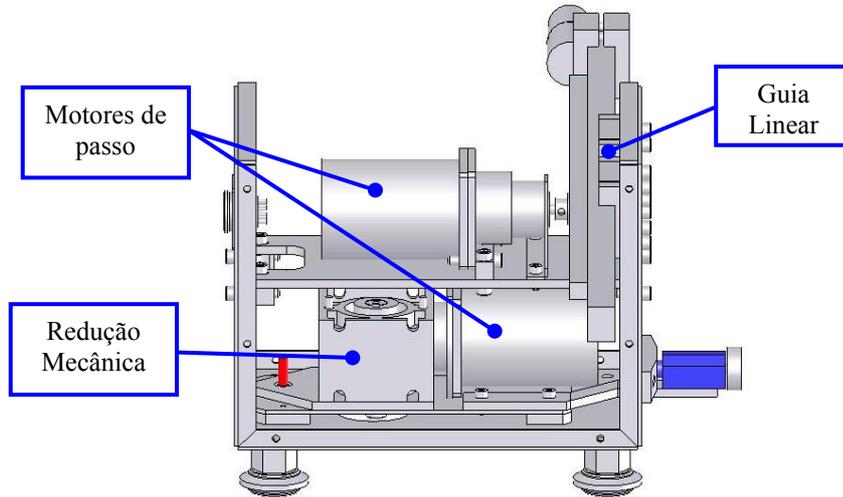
Desenho em CAD da parte mecânica do “Tartilope V2”.
